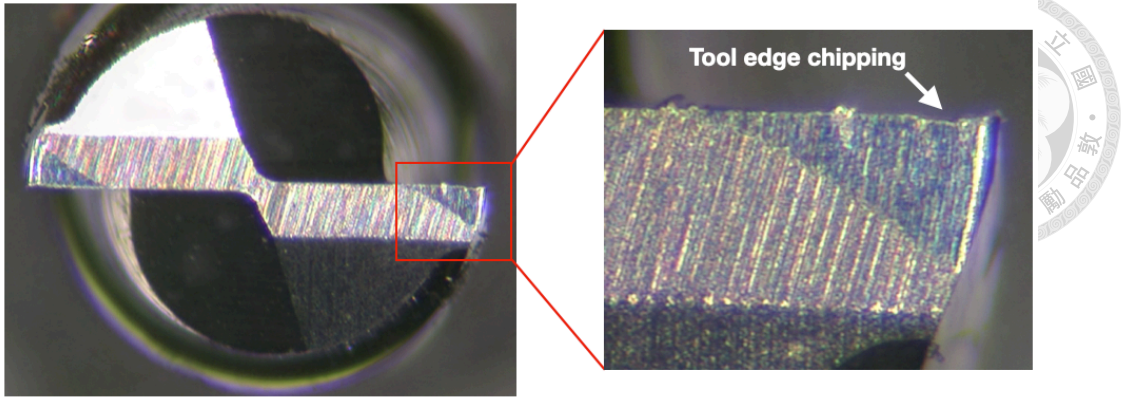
等進給率槽銑加工 – 進給率 800mm/min 切削長度 2700mm 後之刀具磨耗
